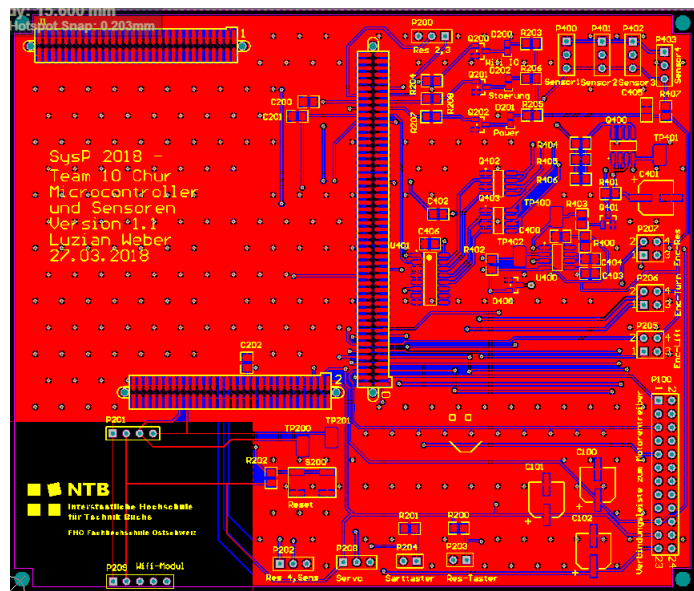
PCB obere Printplatte, schwarzer Bereich: WLAN Modul
